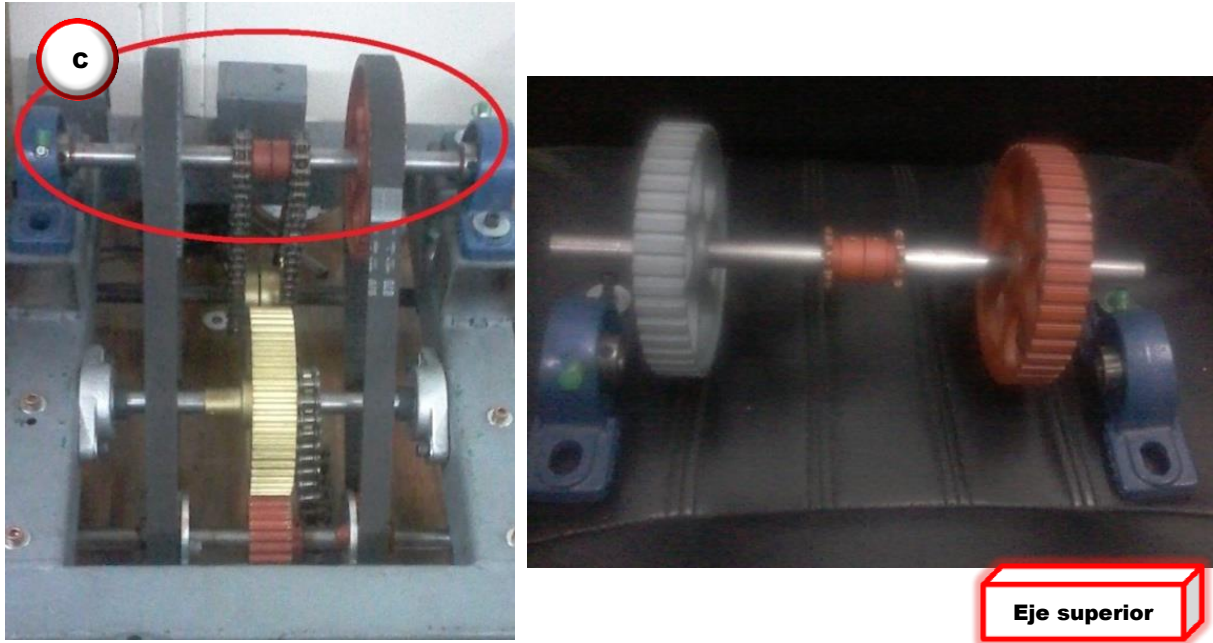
Componentes de la polea dentada y pieza final ensamblada
